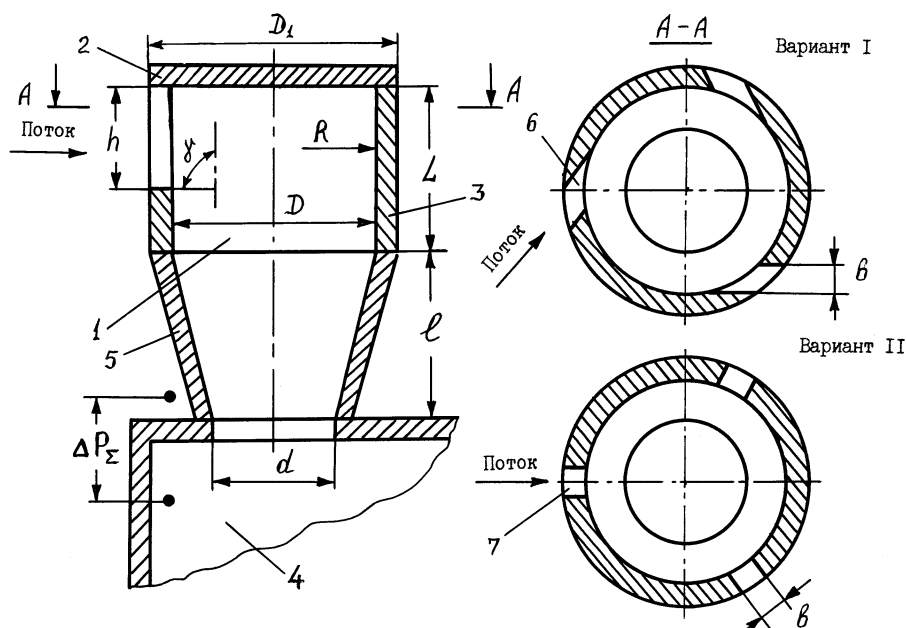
Обобщенная схема макетных образцов закручивающих устройств с тангенциальными (вариант I) и радиальными (вариант II) каналами: 1 – камера; 2 – торцевая крышка; 3 – цилиндрическая часть камеры; 4 – ресивер лабораторной установки; 5 – конфузорная части камеры; 6 и 7 – тангенциальные и радиальные входные каналы соответственно
